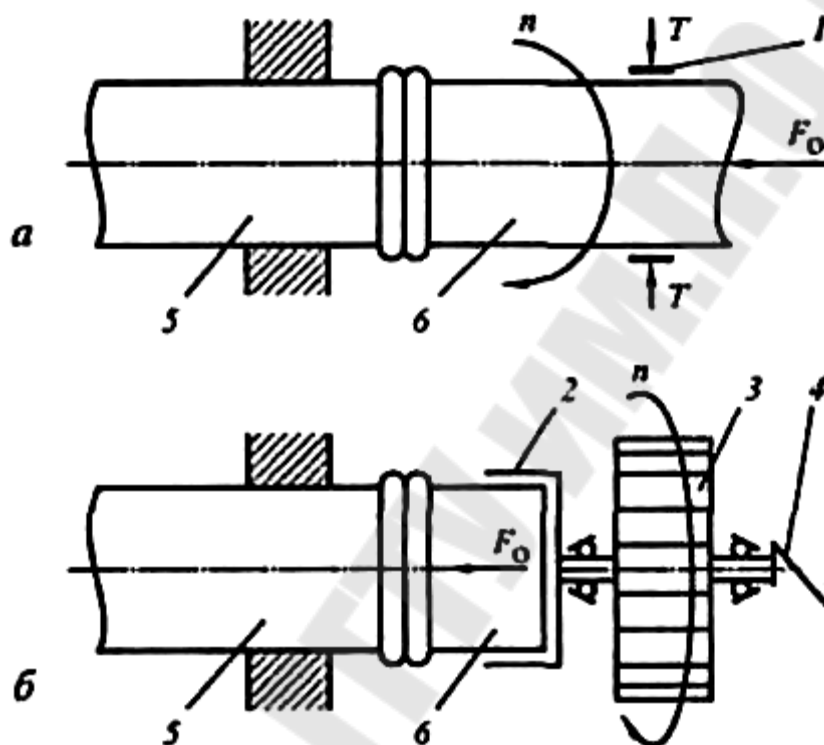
Схема сварки трением: а — обычная; б — инерционная; 1 — тормоз; 2 — захват; 3 — маховик; 4 — муфта сцепления; 5 — неподвижная деталь; 6 — вращающаяся деталь
